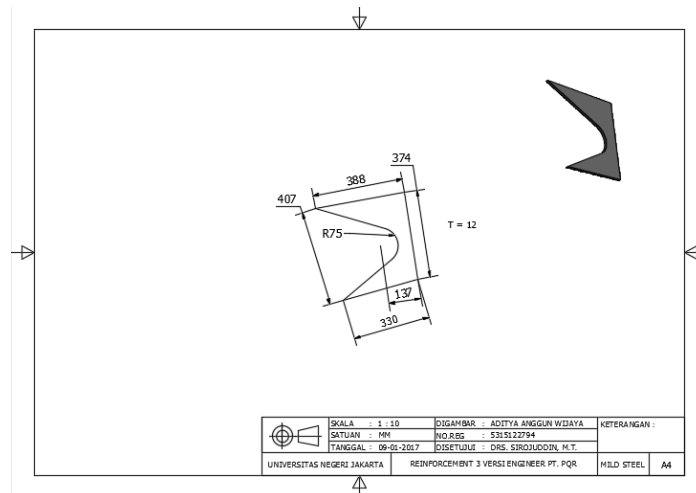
Gambar Dimensi *Part 13 Boom Excavator* Kelas 20 Ton
